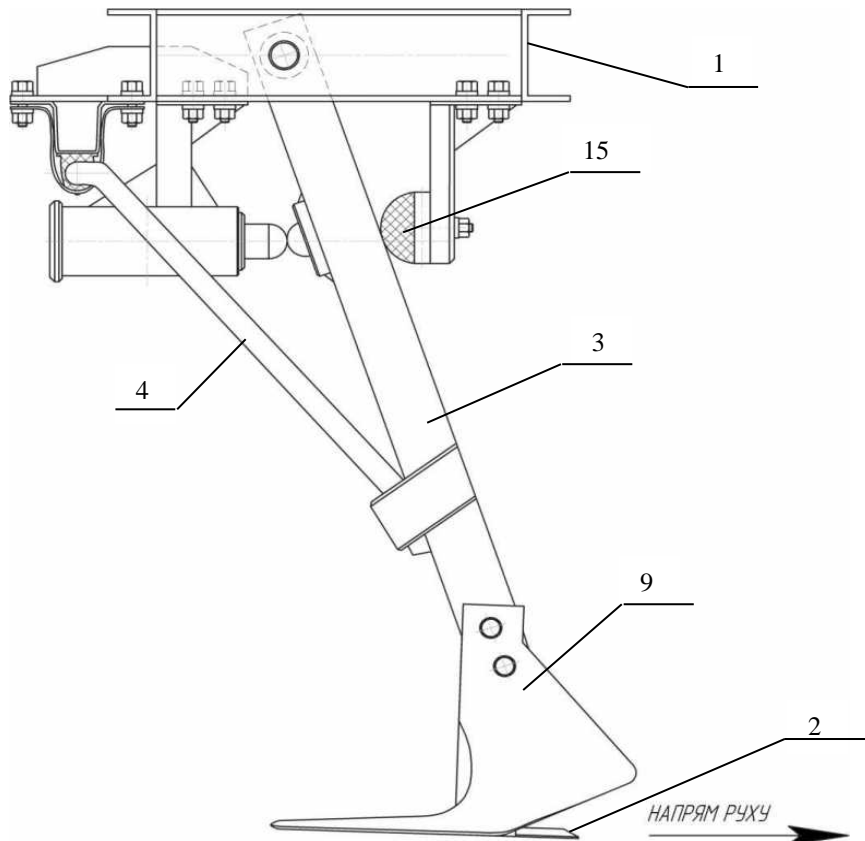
Плоскорізний ґрунтообробний робочий орган (вид збоку).
